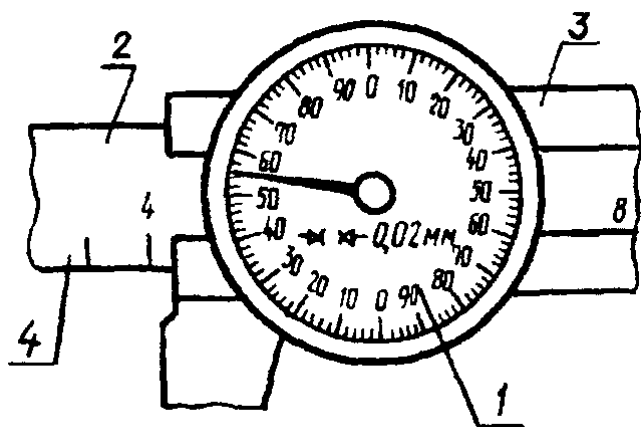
1- кругла шкала відлікового пристрою; 2- штанга; 3- рамка; 4- шкала штанги
